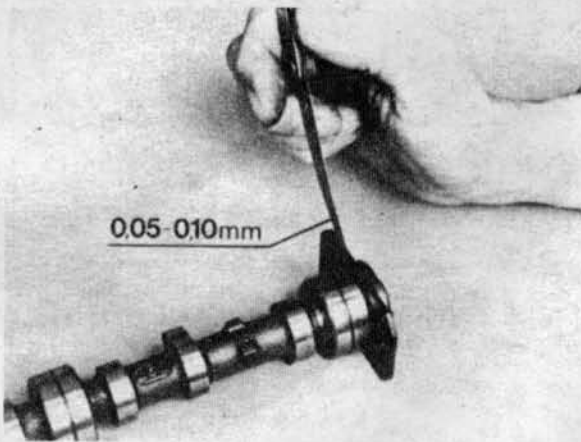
Измерение зазора посадки распредвала двигателей В13/В14
